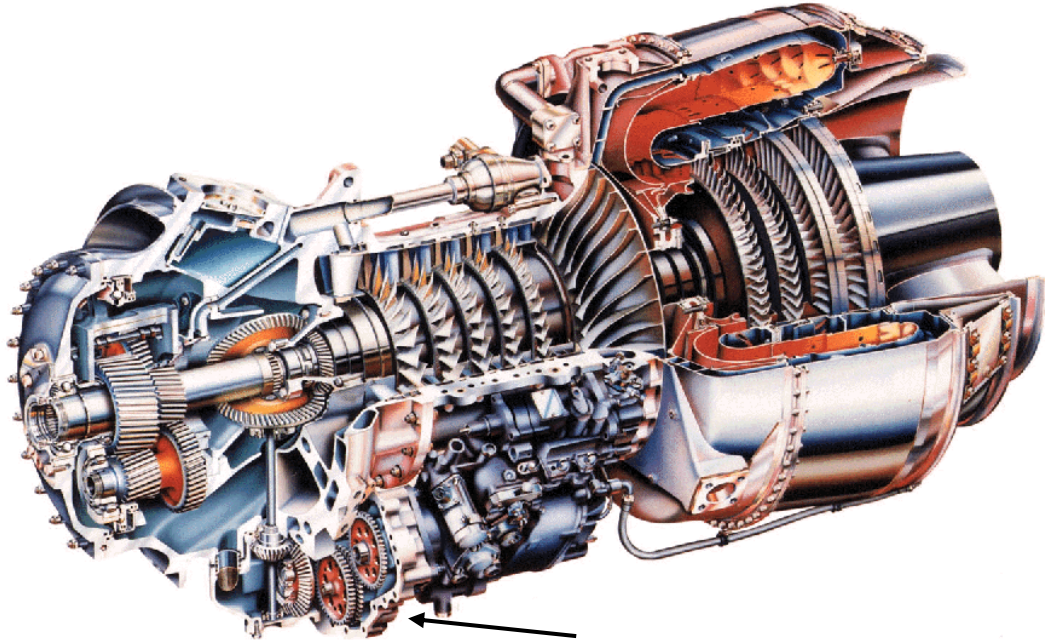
Darstellung des Triebwerks T53 und der Position der N1 *accessory drive gearbox* (siehe Pfeil)
